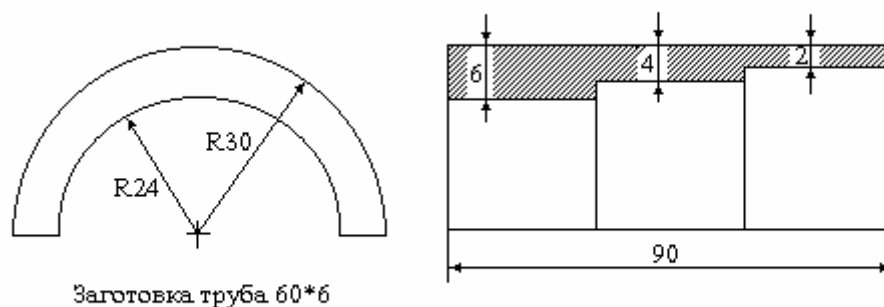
Образец из элемента трубы для настройки шкалы прибора.
